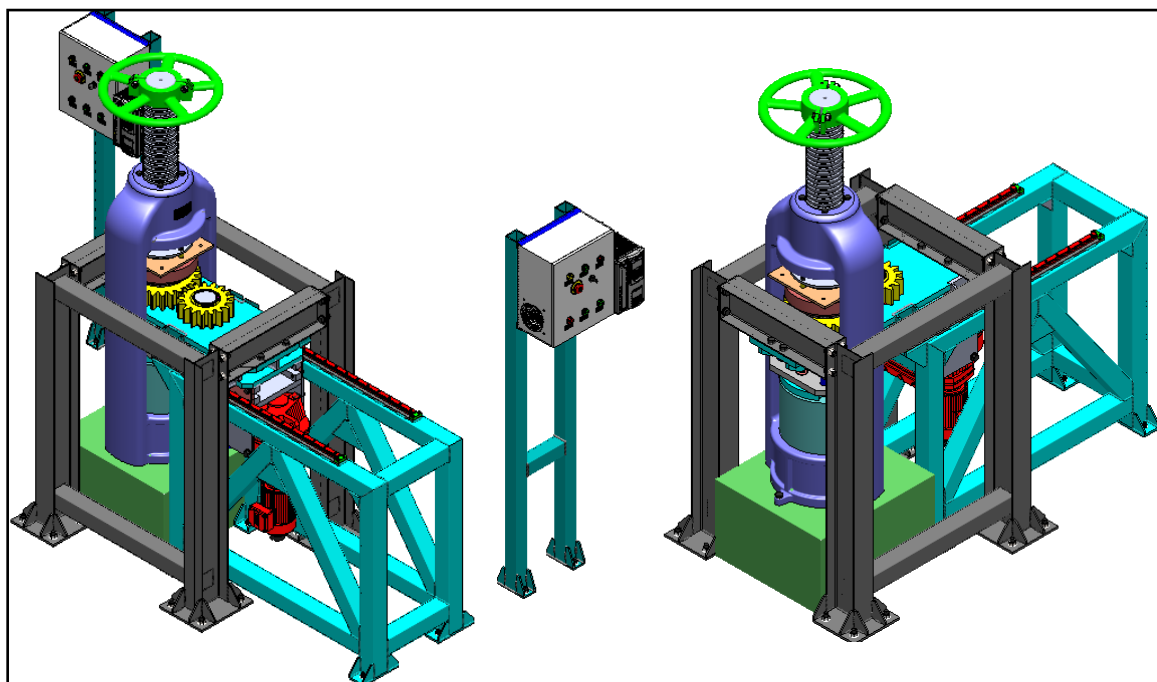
Montagem do equipamento HPT (high pressure torsion) adaptado a uma máquina de ensaio de compressão de 200 T.
